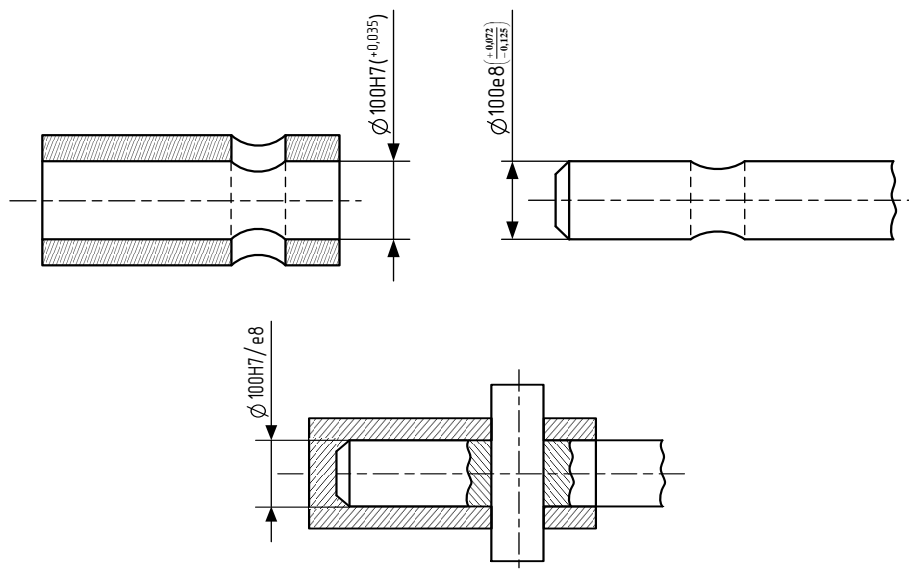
Обозначение на чертеже допусков и посадок
